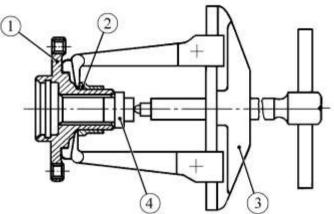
Спрессовка внутреннего кольца подшипника со ступицы переднего колеса:
